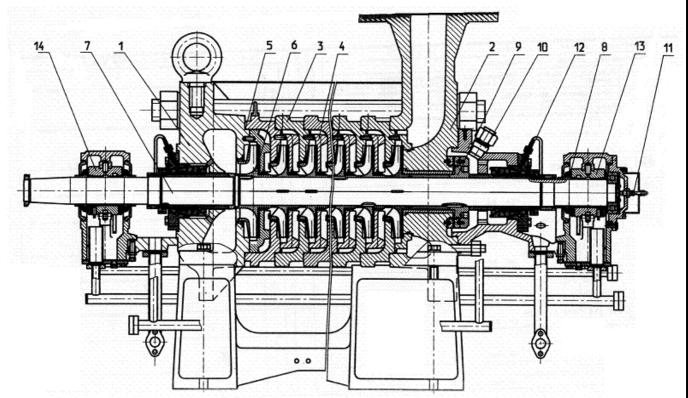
Насос центробежный ЦНС 240 – 1900 – 2Т ТУ У 3.19–05747991–95 Опорами ротора служат подшипники скольжения 13 и 14 с принудительной смазкой.
